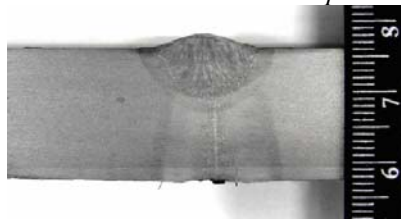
Макрошлиф шва стали X60 после контактной сварки корня шва с последующей двухпроходной сваркой ИДСПЭ проволокой Sv-08Г2С диаметром 2 мм в смеси 82 %  $Ar + 18\% CO_2$ .
